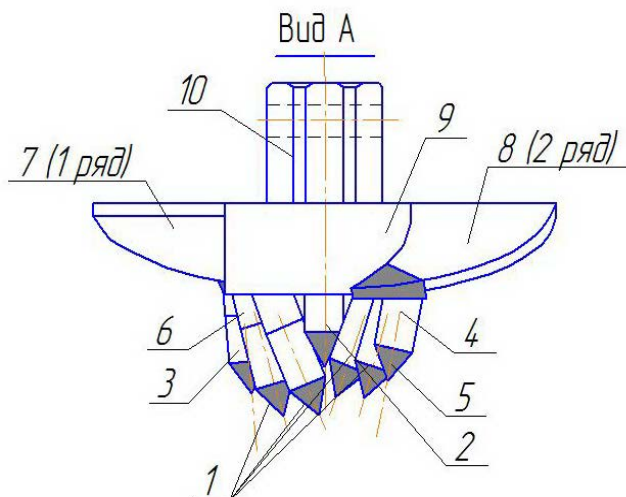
Ступенчатое расположение резцов. 1,3 и 4 – рабочие резцы; 2 – центральный резец; 5 – твердосплавные режущие пластины; 6 – дополнительная вставка; 7 – первый ряд; 8 – второй ряд; 9 – корпус долота; 10 – хвостовик.
